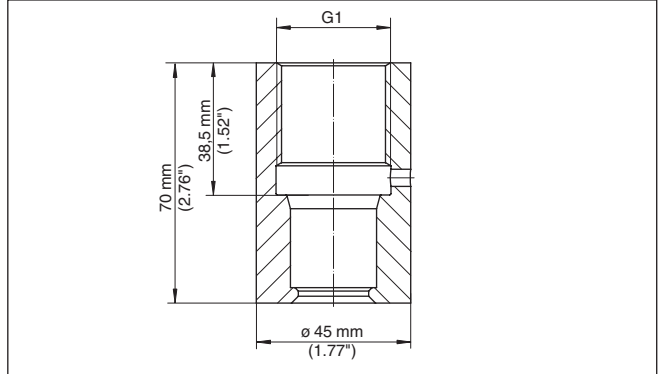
Maße Einschweißstutzen G1 geeignet für PASVE (für beide zuvor aufgeführte Ausführungen) - VEGABAR 82
